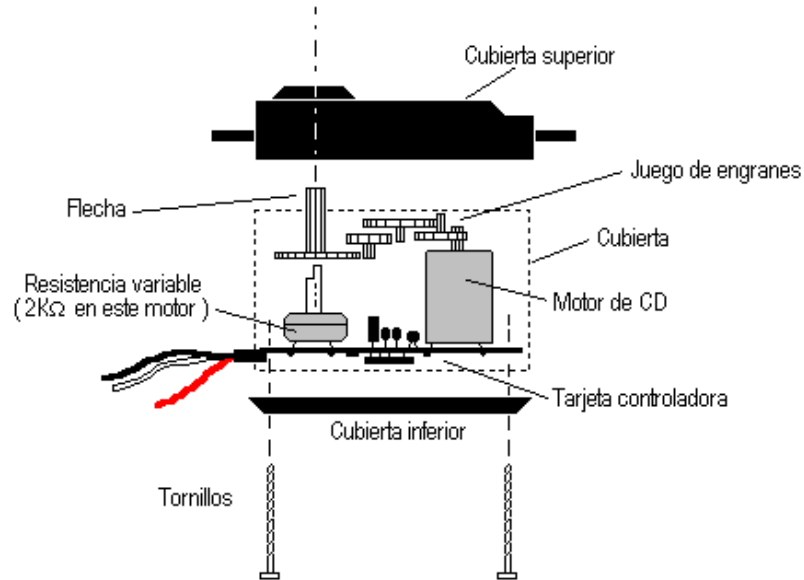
Componentes de un servomotor rotacional [ser17a].
